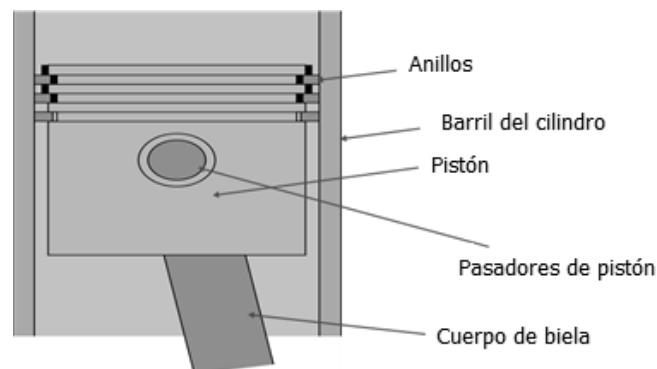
Piezas que componen la cámara de combustión de un cilindro (Carrie, 1999).
